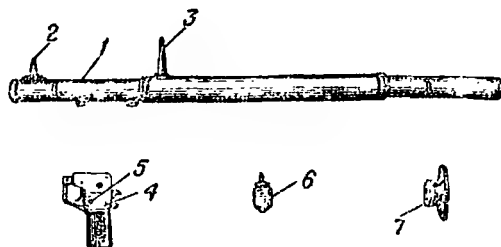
Основные части и механизмы ручного противотанкового гранатомета: 1 — ствол; 2 — мушка; 3 — прицельная рамка; 4 — ударно-спусковой механизм; 5 — предохранитель спуска; 6 — бойковый механизм; 7 — предохранитель ствола
